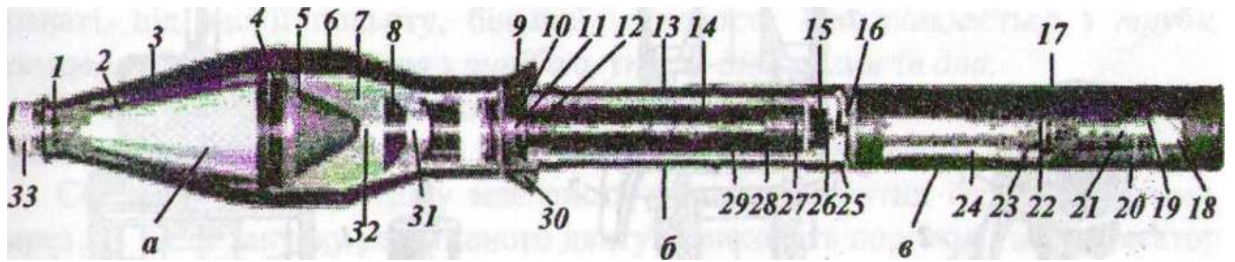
Постріл ПГ-7В: *а* — головна частина; *б* — реактивний двигун; *в* — пороховий заряд; 1 - ізоляційна втулка; 2 - струмопровідний конус; 3 - обтікай; 4 - ізоляційне кільце; 5 - вирва; 6 - корпус; 7 - розривний заряд; 8 - втулка заряду; 9 - сопловий блок; 10 - герметизатор; 11 - фіксатор; 12 - шайба; 13 - труба; 14 - пороховий заряд реактивного двигуна; 15 - дно; 16 - цоколь; 17 - гільза з паперу; 18 - пиж із пінопласту; 19 - турбінка; 20 - стрічковий нітроглицериновий порох; 21 - трасер; 22 - хрестовина стабілізатора; 23 - вісь крила стабілізатора; 24 - крило стабілізатора; 25 - виступ із різьбою; 26 - осьовий канал; 27 - капсуль-запальник; 28 - радіальний канал; 29 - піросповіднювач; 30 - сопловий отвір; 31 - донна частина підривана; 32 -
